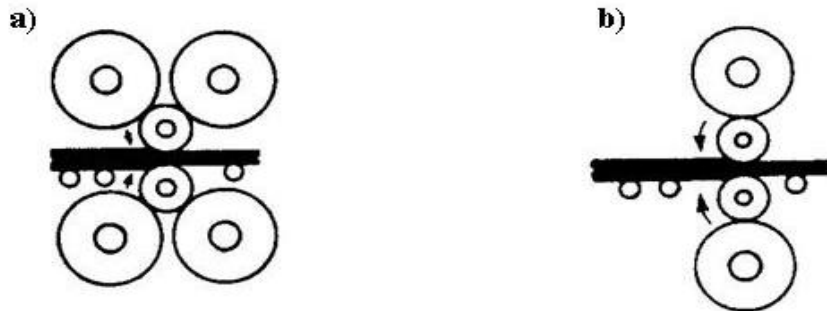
a) Molino laminador en conjunto y b) Molino Laminador de cuatro rodillos
